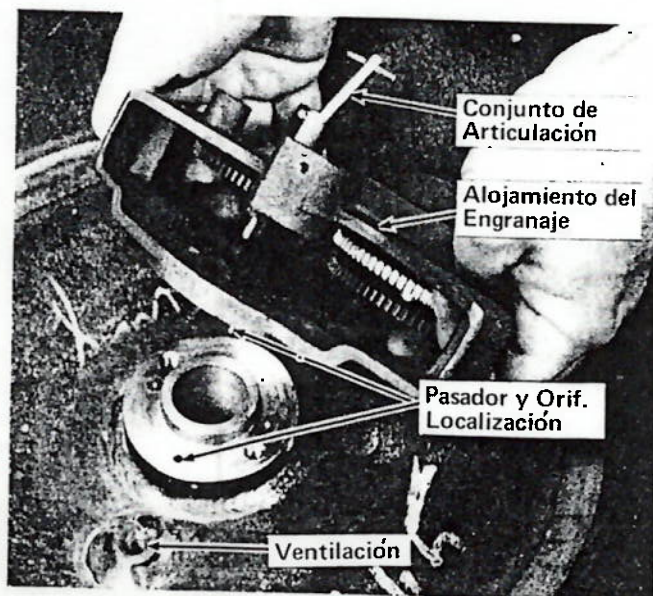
REMOCIÓN DEL ALOJAMIENTO DEL ENGRANAJE.
